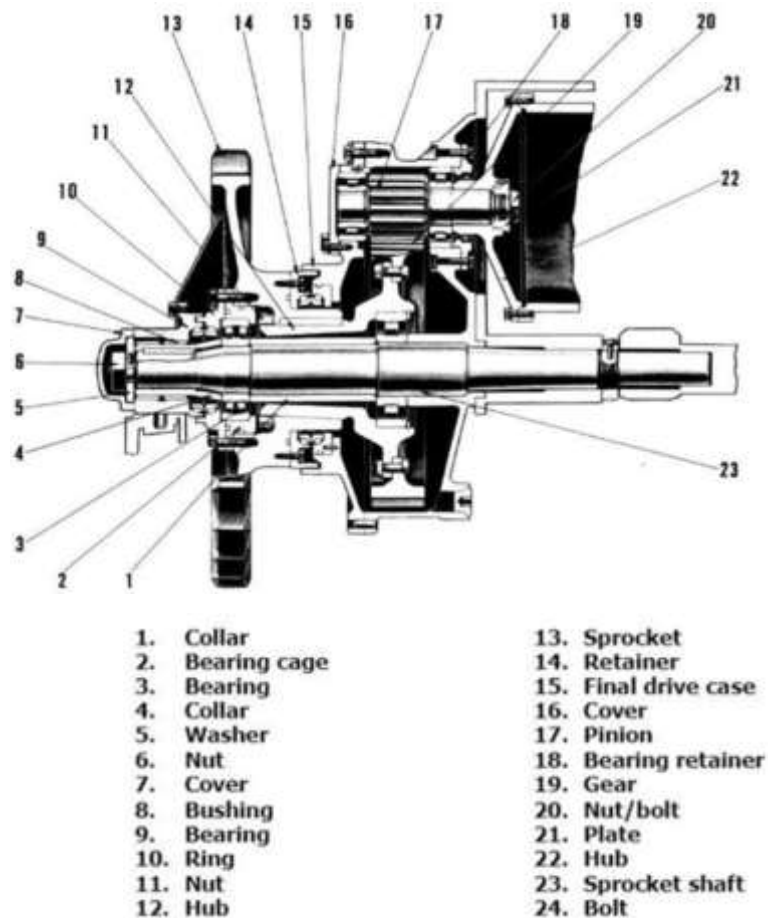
9 Final drive tipe Single Reduction Rotated Final drive Shaft (D31A-17, D319Q-17)
